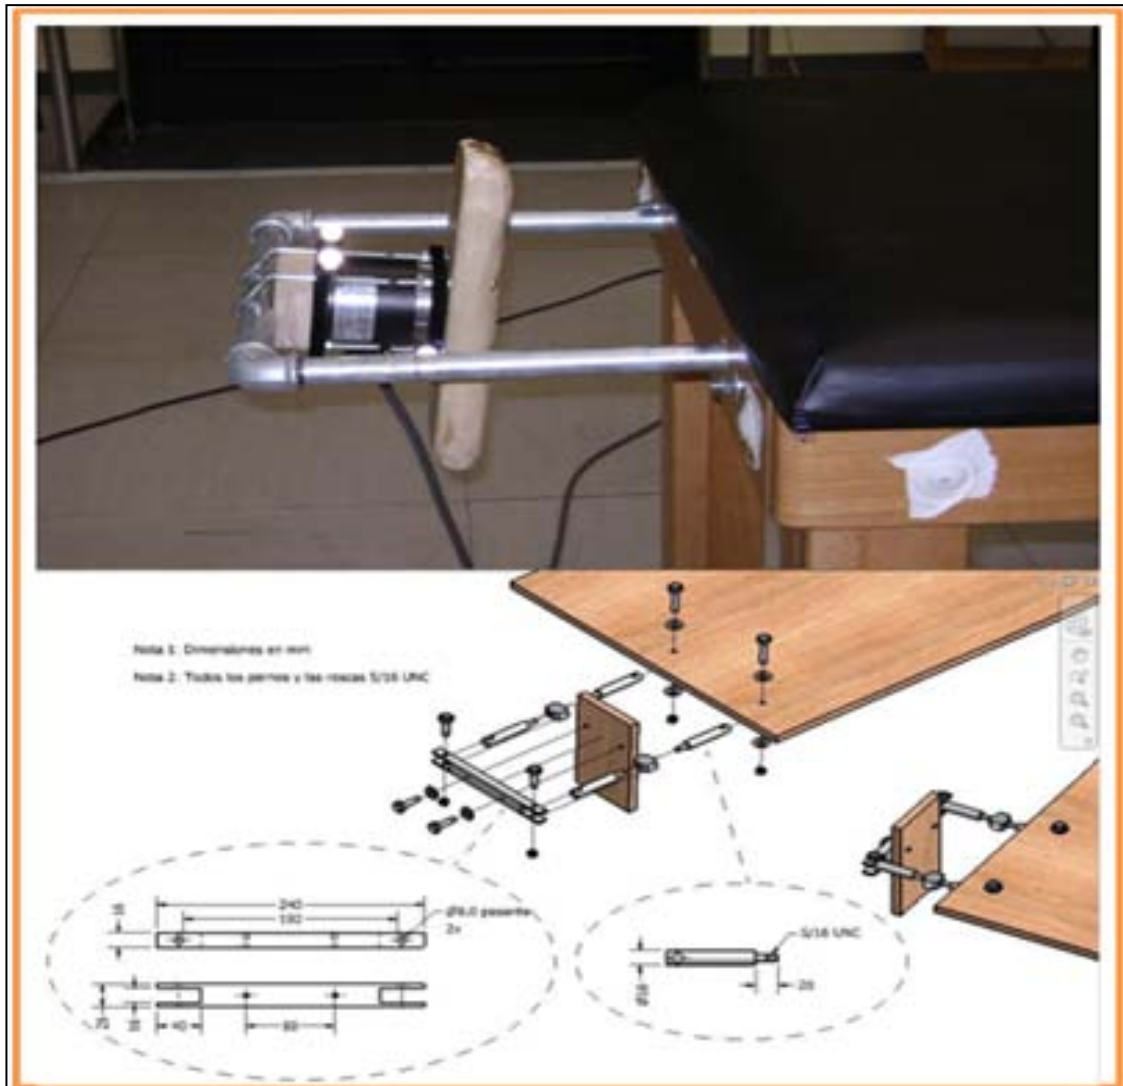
Diseño de la ubicación del dinamómetro (celda de carga con 6 componentes, Bertec Inc) en la camilla de fisioterapia, para la medición de la fuerza isométrica del Gastrocnemio en posición prona. Diseño del grupo de Biomecánica de la Universidad del Valle de Cali- Colombia.
